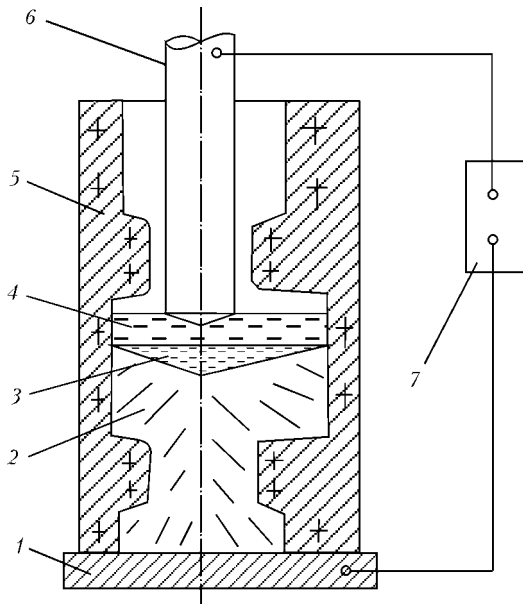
Схема ЭШЛ заготовок корпусов задвижек с фланцами на концах патрубков: 1 — поддон; 2 — выплавляемая заготовка; 3 — металлическая ванна; 4 — шлаковая ванна; 5 — кристаллизатор; 6 — расходный электрод; 7 — источник питания
